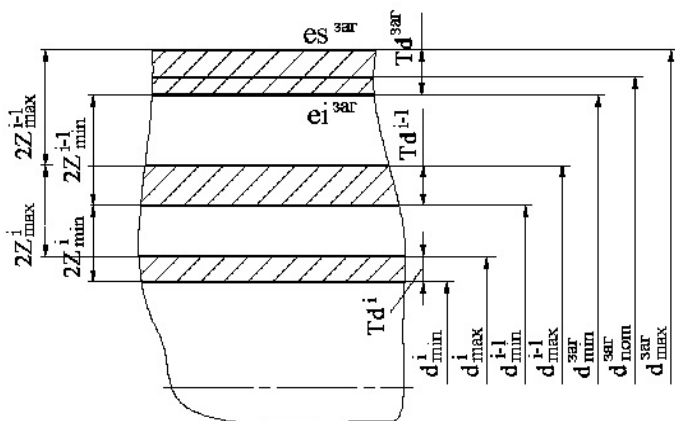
Схема расположения припусков и операционных размеров для обработки вала на настроенном станке
